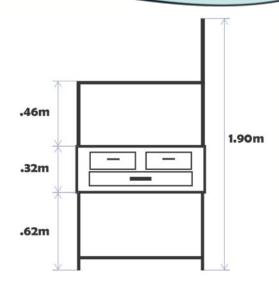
Mesa de trabajo utilizada con dimensiones generales.
